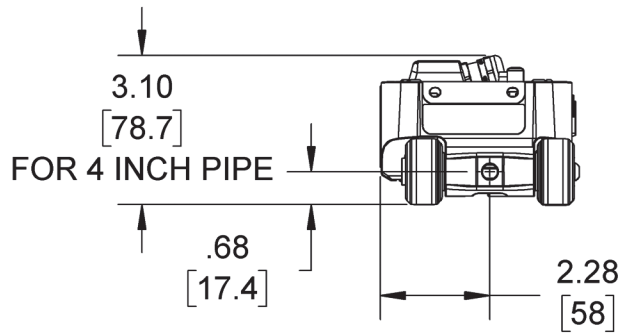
Dimensioni della vista frontale HydroFORM senza encoder dell'indice e senza ScanDeck
